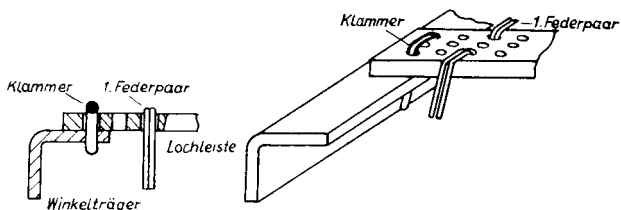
Vorschlag für die Befestigung der Federleiste im Gerät
